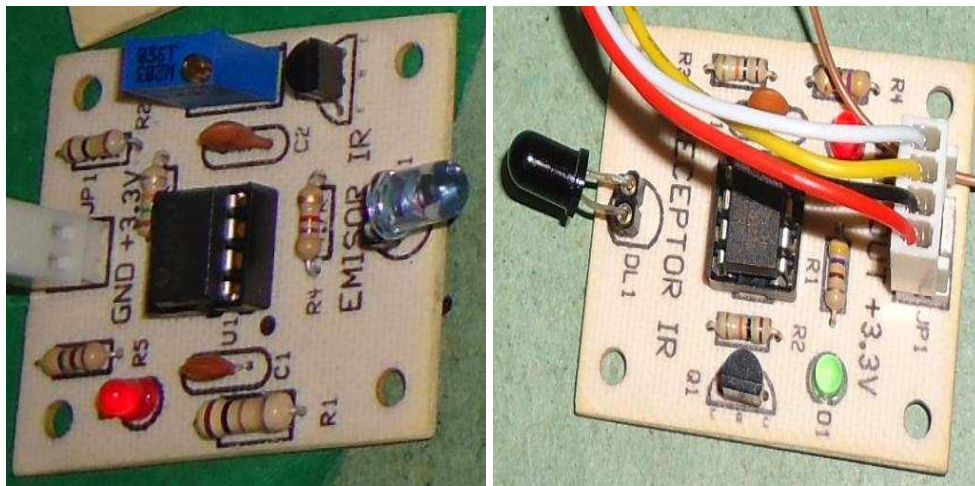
Tarjeta electrónica al final del proceso de soldadura
